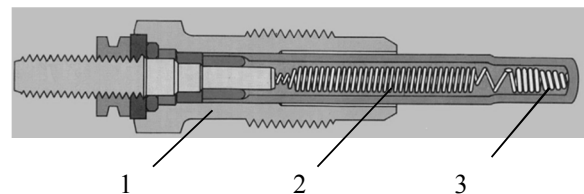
Конструкція свічок розжарювання з регулюючою спіраллю; 1 - металевий корпус; 2 - регулююча спіраль; 3 - нагрівальна спіраль
